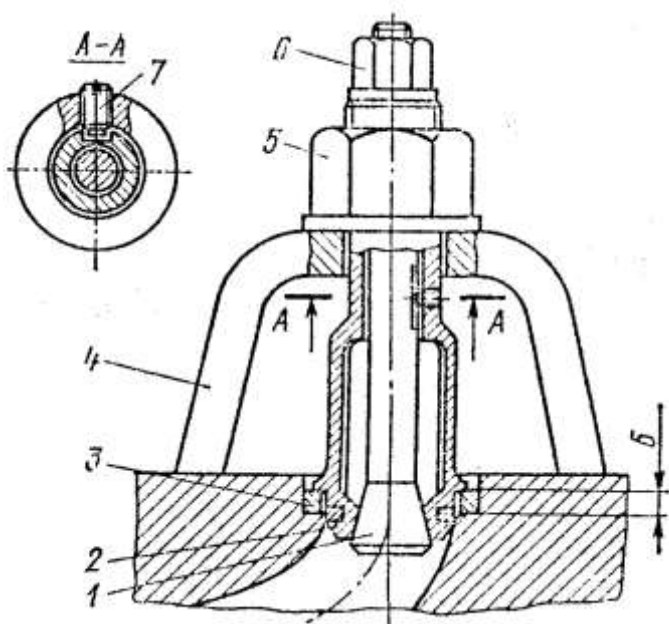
Съемник для выпрессовки седла клапана из головки цилиндров: 1 - конус; 2 - цанга; 3 - вставка; 4 - корпус; 5, 6 - гайки; 7 - винт; Б - размер, равный высоте седла.
